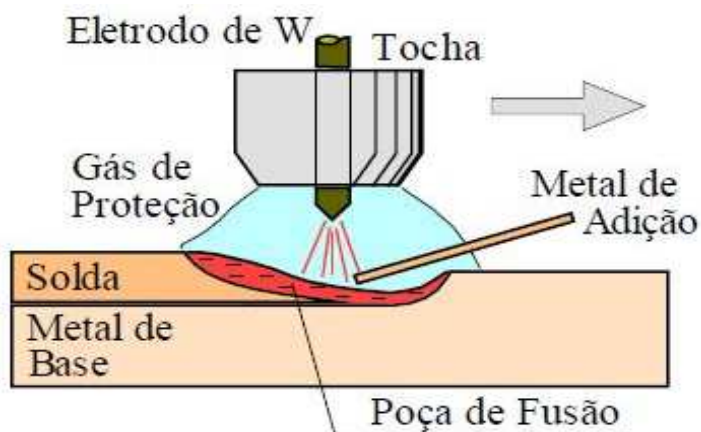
Representação esquemática da soldagem TIG [Marques et al., 2005].
